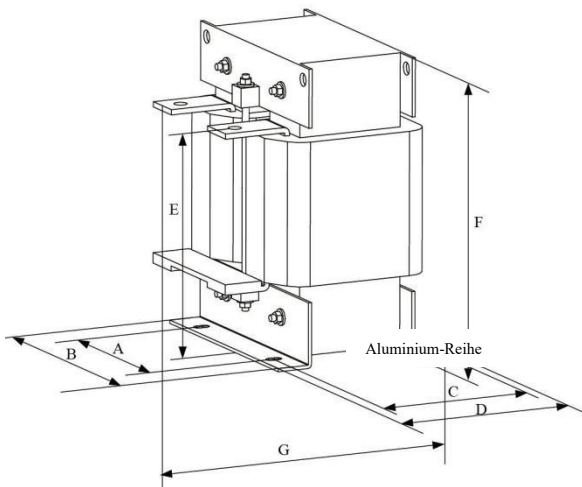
Maßzeichnung der externen Gleichstromdrossel
